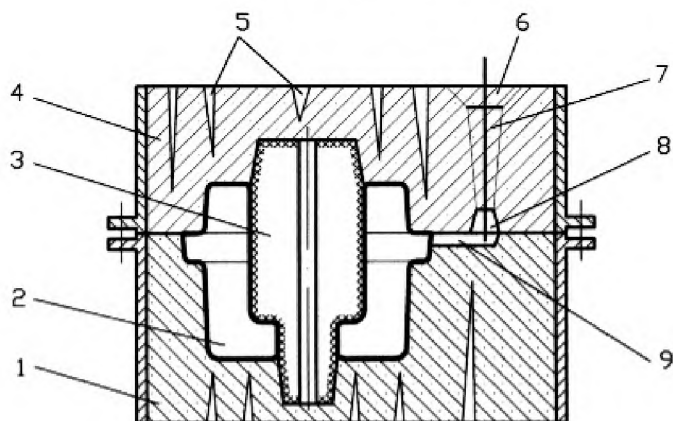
Эскиз литейной формы для изготовления отливки по варианту 3:
